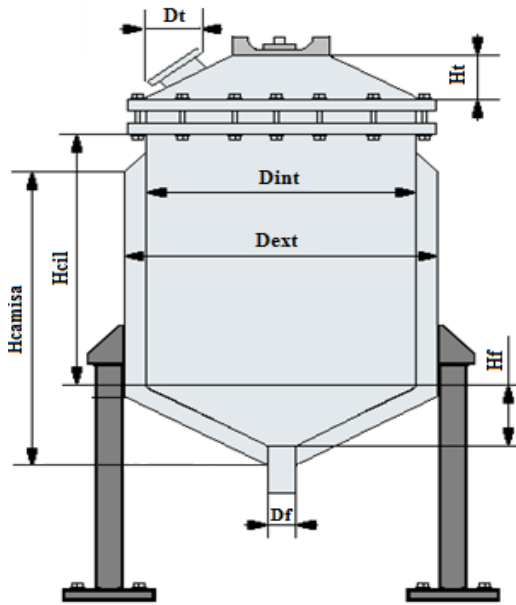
Vista exterior del reactor a escala planta piloto.
